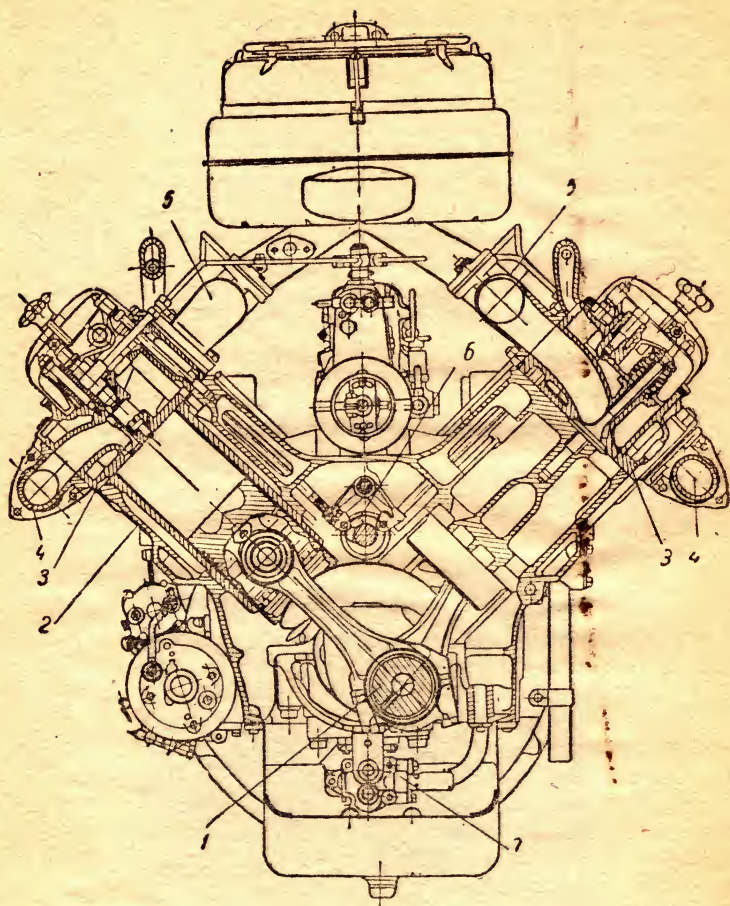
Поперечный разрез двигателя ЯМЗ-236:
